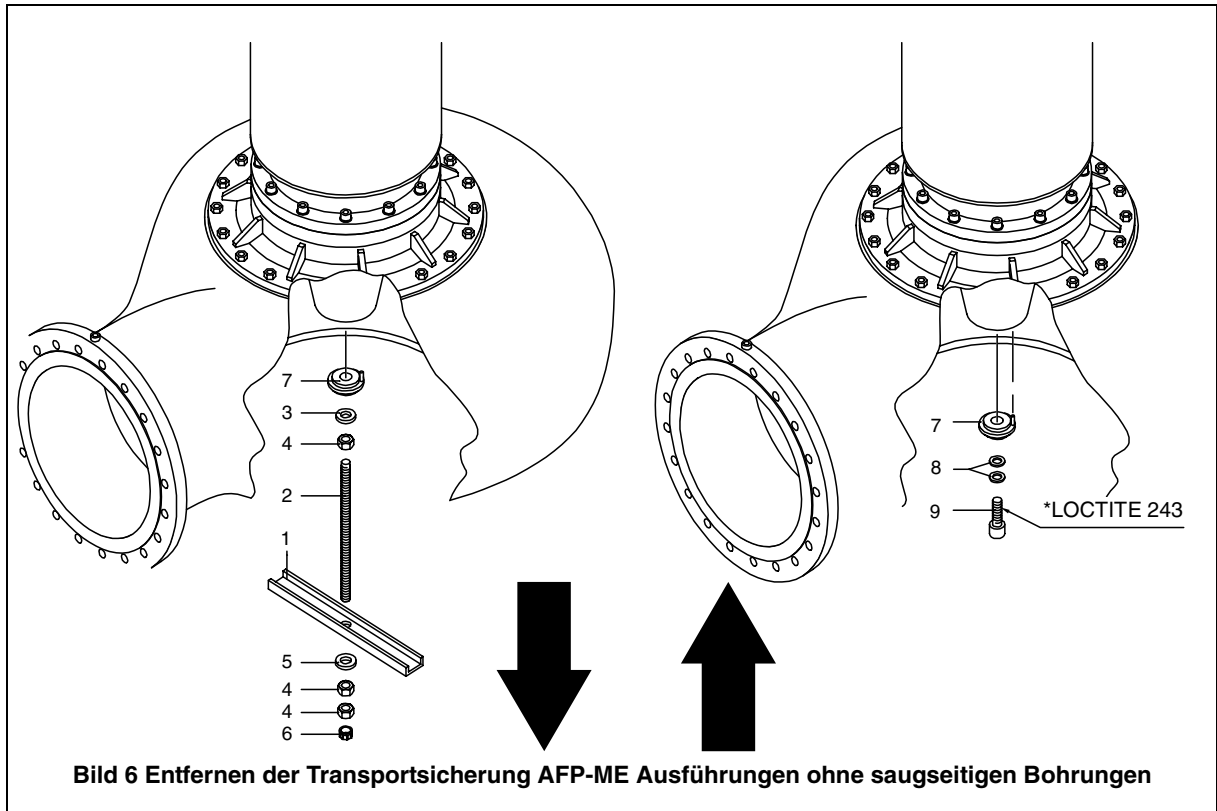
Entfernen der Transportsicherung AFP-ME Ausführungen ohne saugseitigen Bohrungen
